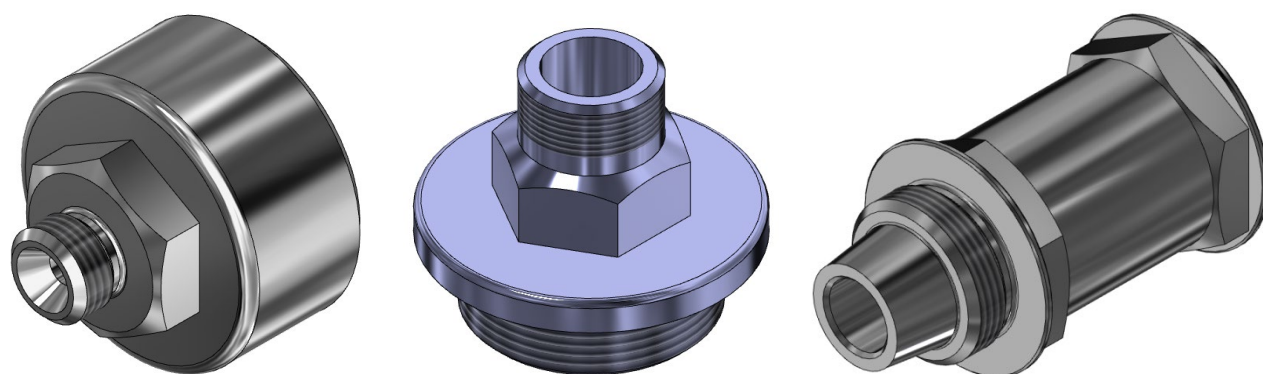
3D-моделі накривки, штуцера та корпусної деталі.
